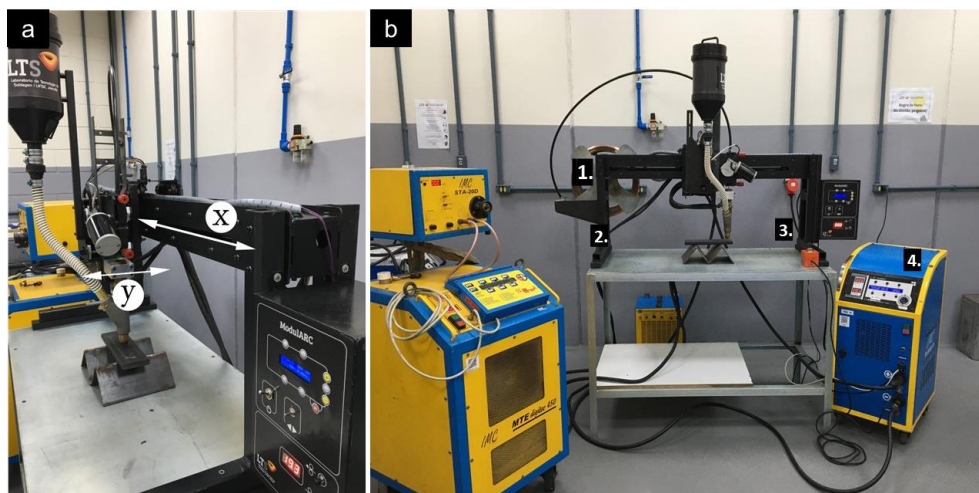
Tocha (a) e Bancada (b) de soldagem SAW do LTS
